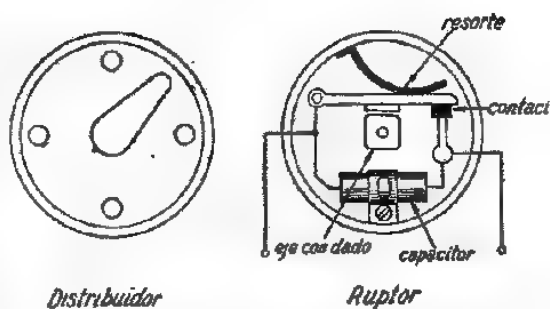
Vista esquemática del distribuidor y el ruptor de un sistema de encendido para un motor a explosión.
